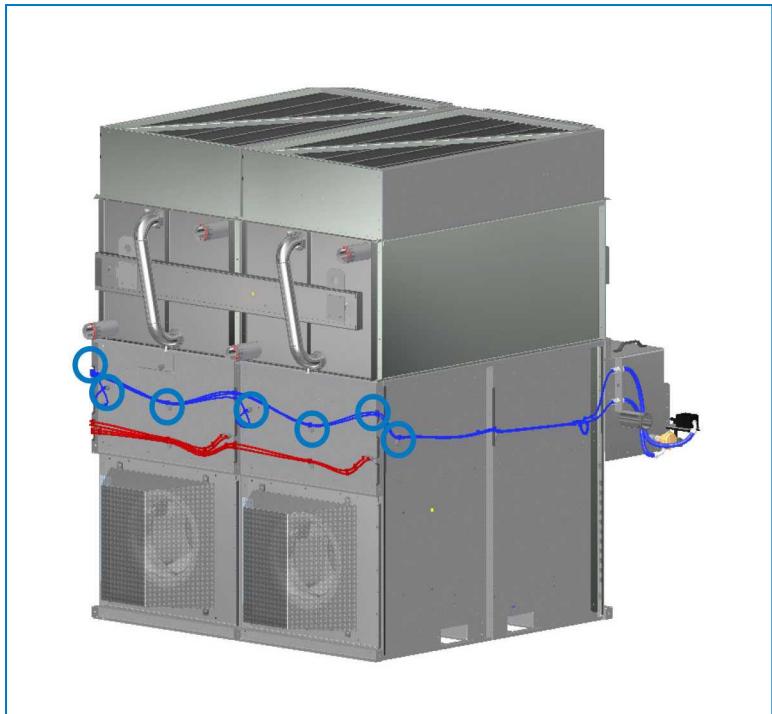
Прокладка провода связи и провода компонента для вентилятора
